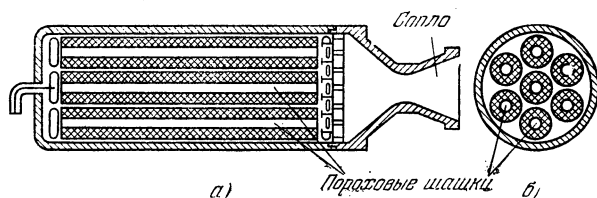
Ракетный двигатель твердого топлива: а) продольный и б) поперечный разрез.
